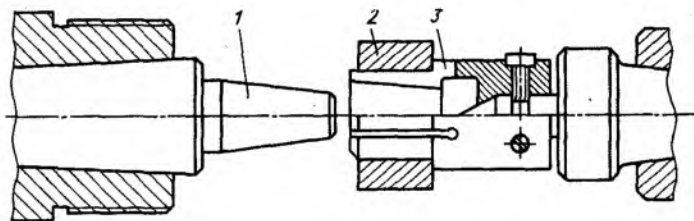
Цанговая оправка для переустановки заготовок без остановки вращения шпинделя
